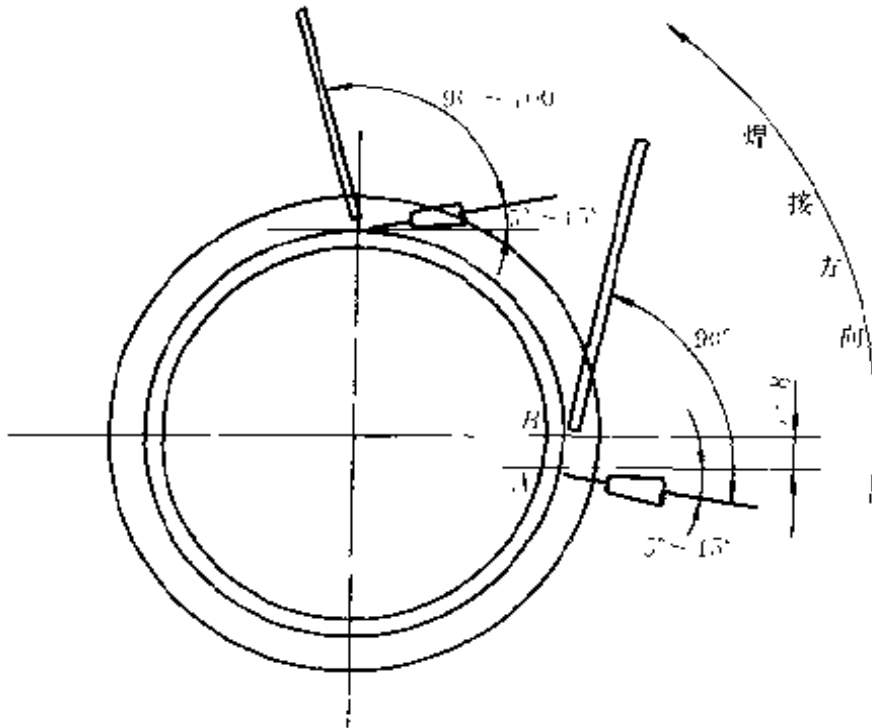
13 小管水平固定右半部 3 点位置至 12 点位置的外填丝 TIG 焊
